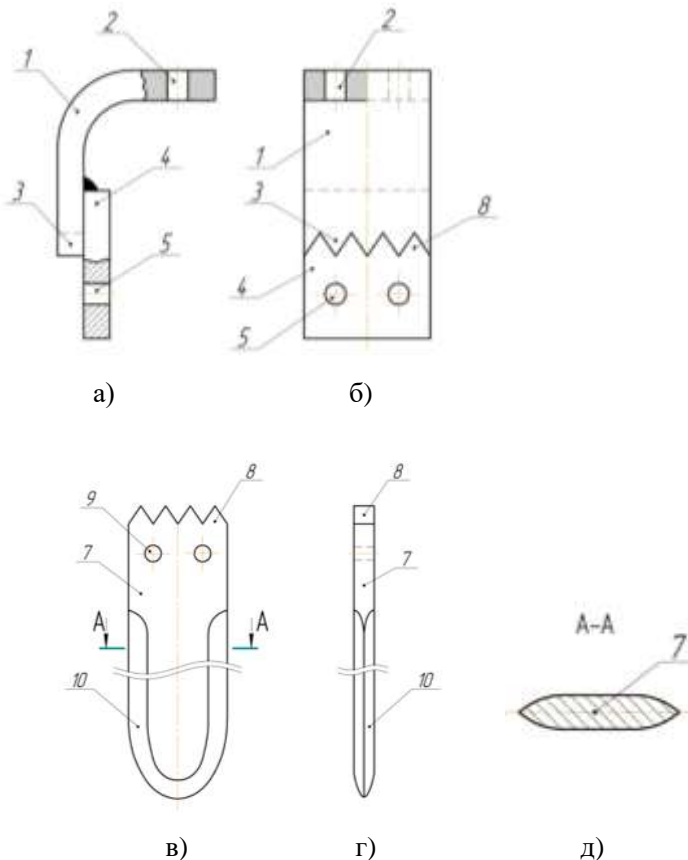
Схема рабочий орган почвообрабатывающей фрезы.
